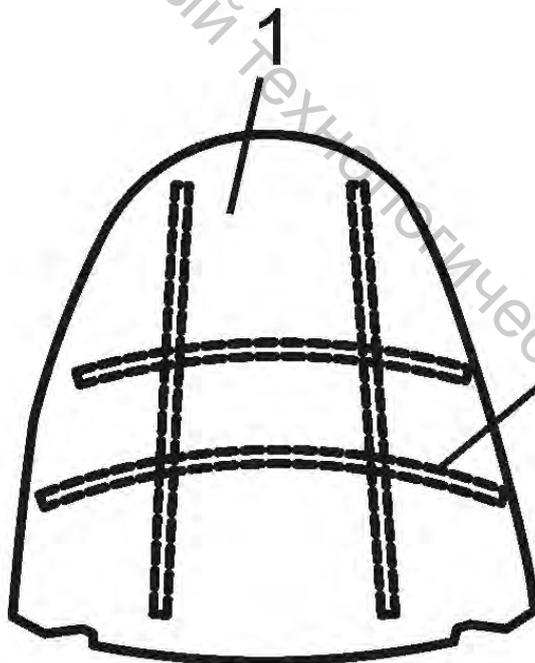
Деталь носка заготовки верха обуви:
